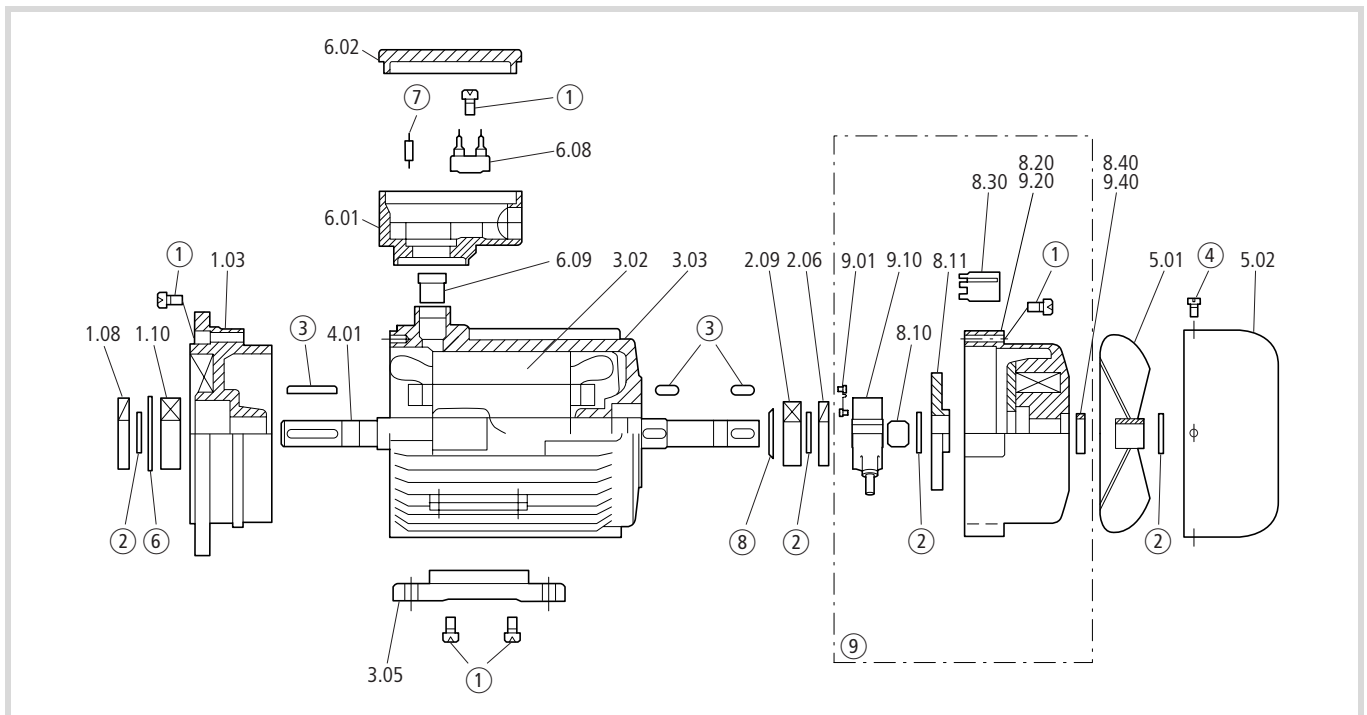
Explosionszeichnung Baugröße 63 bis 132
